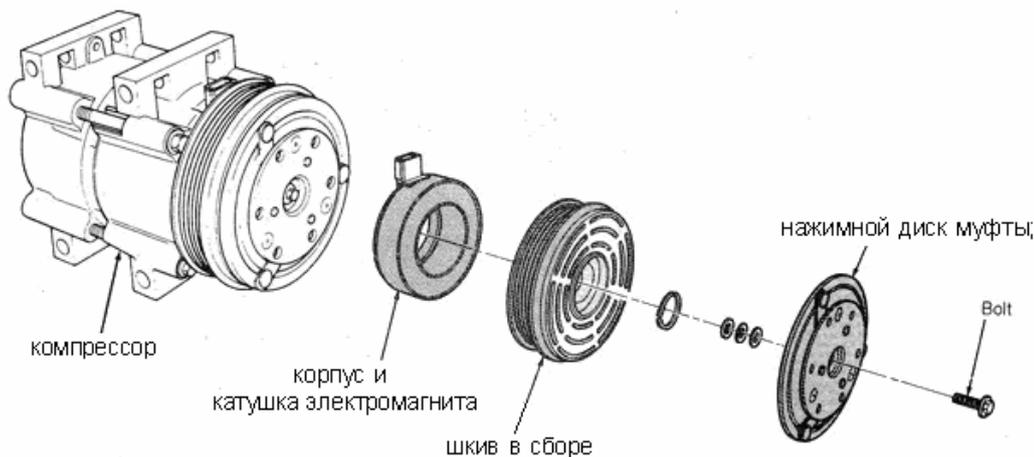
Привод десятицилиндрового компрессора автомобиля Форд
